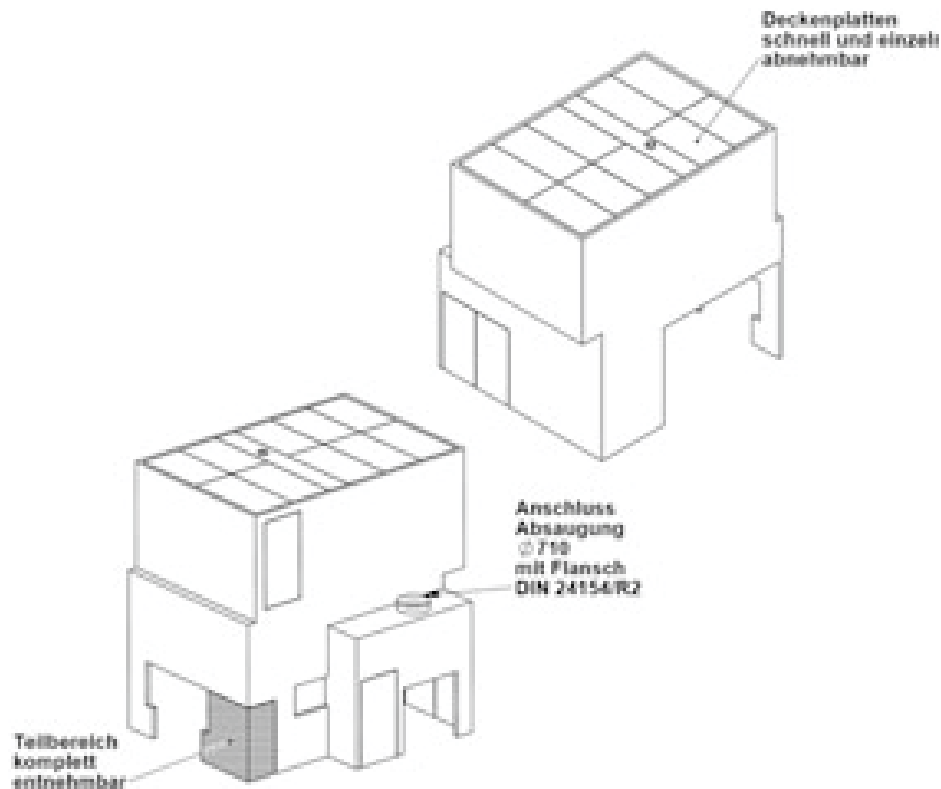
Konzept zur Einhausung mit demontierbaren Schallschutzelementen
